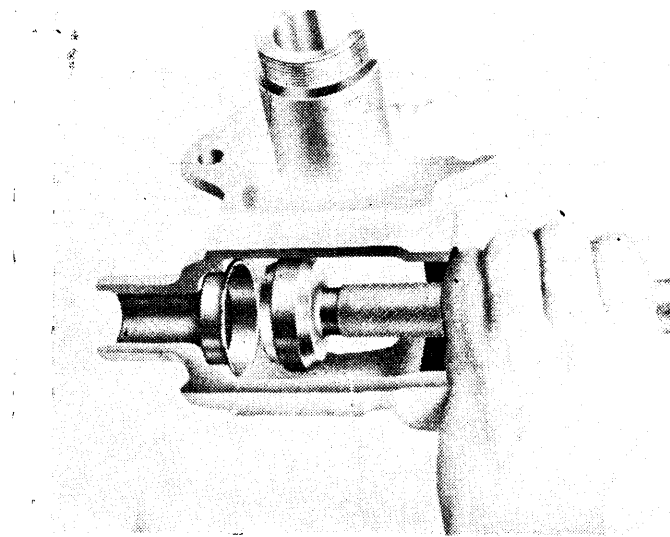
Einpressen der Aussenringe in das Lenkgehäuse mittels Vorrichtung D-54.
